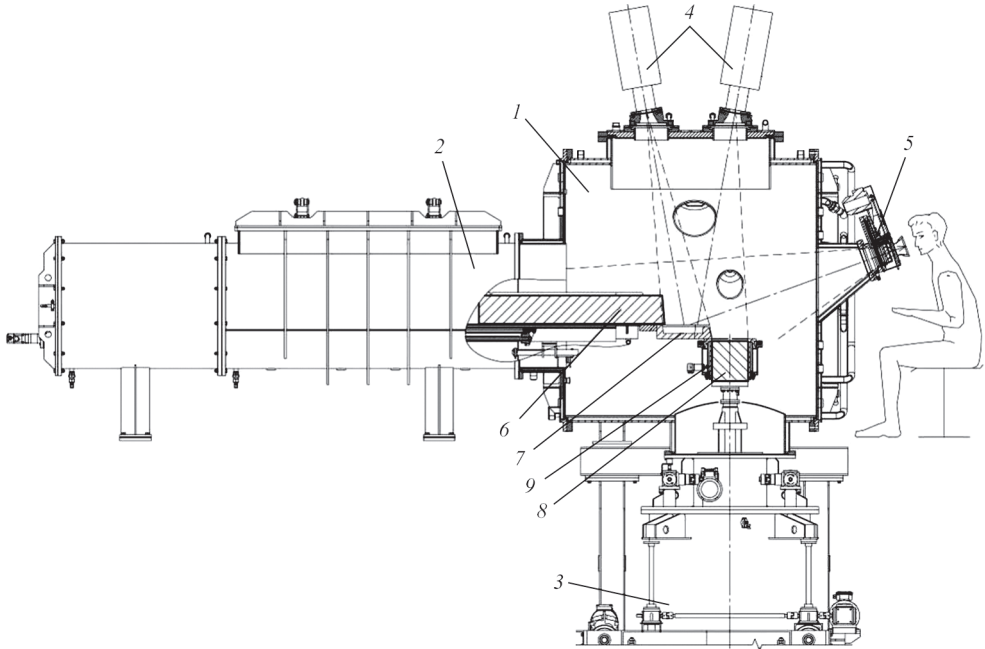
Схема електронно-променевої установки: 1 — камера плавки; 2 — камера завантаження; 3 — механізм вертикальної подачі заготовки; 4 — електронно-променева гармата; 5 — оглядова система; 6 — заготовка; 7 — проміжна ємність; 8 — зливков; 9 — кристалізатор
